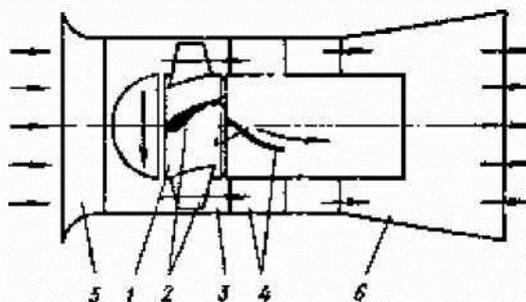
Схема осевого вентилятора: 1 - рабочее колесо; 2 - лопатки рабочего колеса; 3 - кожух; 4 - спрямляющий аппарат; 5 - коллектор; 6 - диффузор
